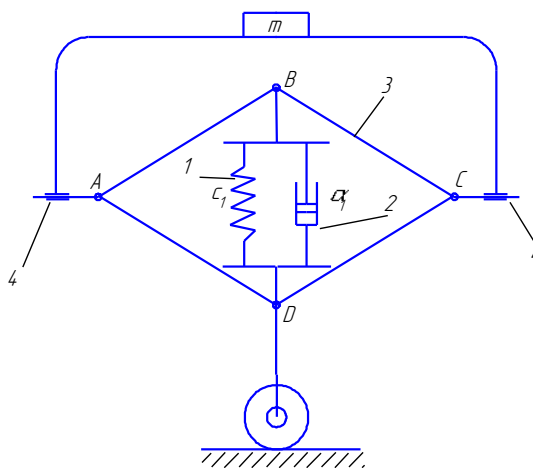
Кінематична схема пружно-демпферного модуля підвіски транспортного засобу на основі чотириланкового важільного ромбовидного механізму: 1 – пружний елемент, 2 – демпферний елемент, 3 – чотириланковий важільний ромбовидний механізм, 4 – підшипники кріплення підресореної маси m
